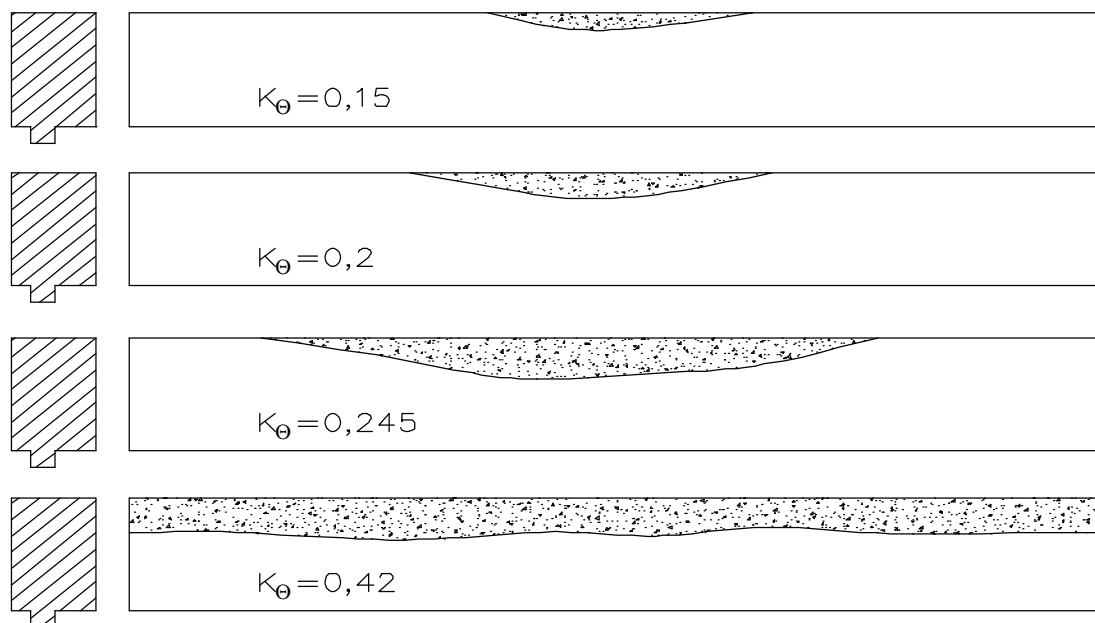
Развертки внутренней цилиндрической поверхности плавающих колец со следами натиров
